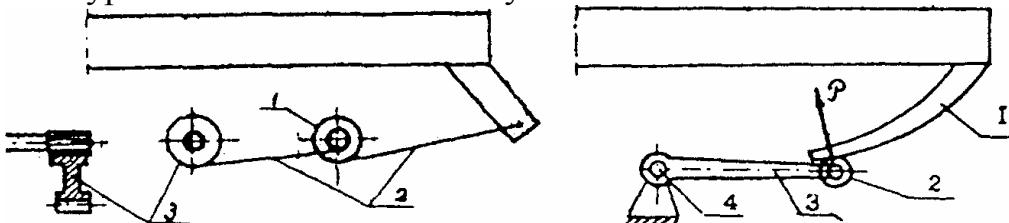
Схема торсионного механизма с редуктором: 1 - редуктор; 2 - гибкая связь; 3 – шкив.
